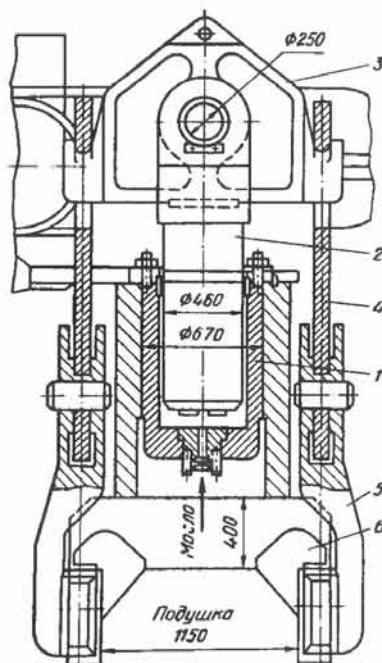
Устройство гидравлического уравновешивания верхнего опорного валка четырехвалковой клети 2500:
